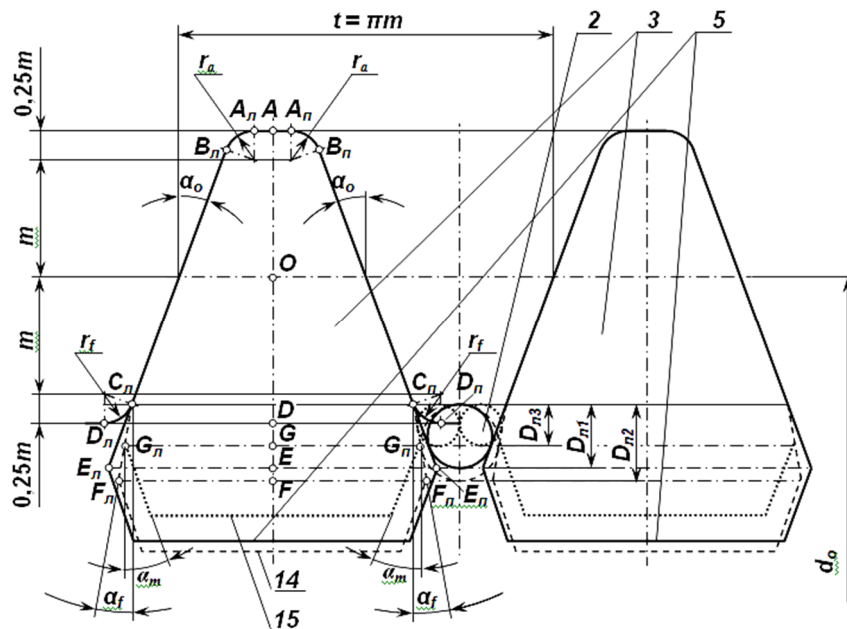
Параметры профиля быстросменных режущих пластин для червячного шевера и пружин, введенных между их ножками
